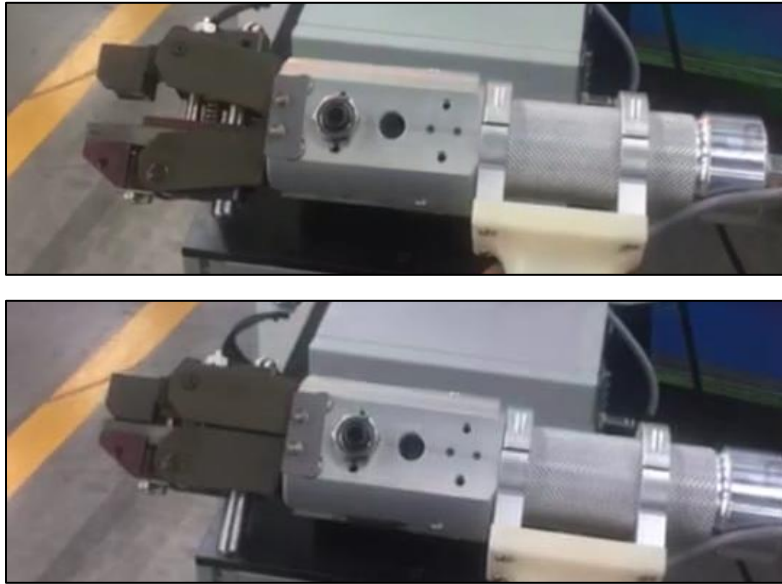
Arriba: Pistola LOKRING posición de abiertas. Debajo: Pistola LOKRING posición cerrada.
